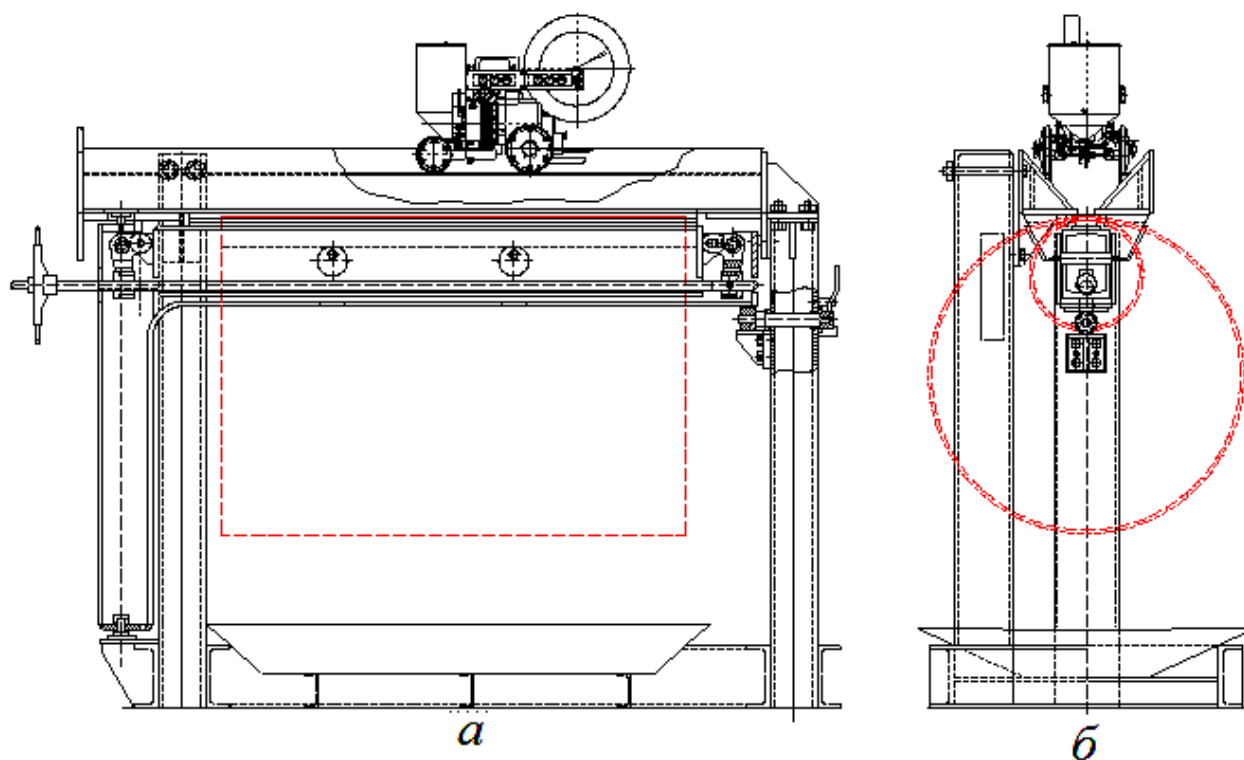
Установка із мідною підкладкою для зварювання обичайок однобічним поздовжнім швом під флюсом:
